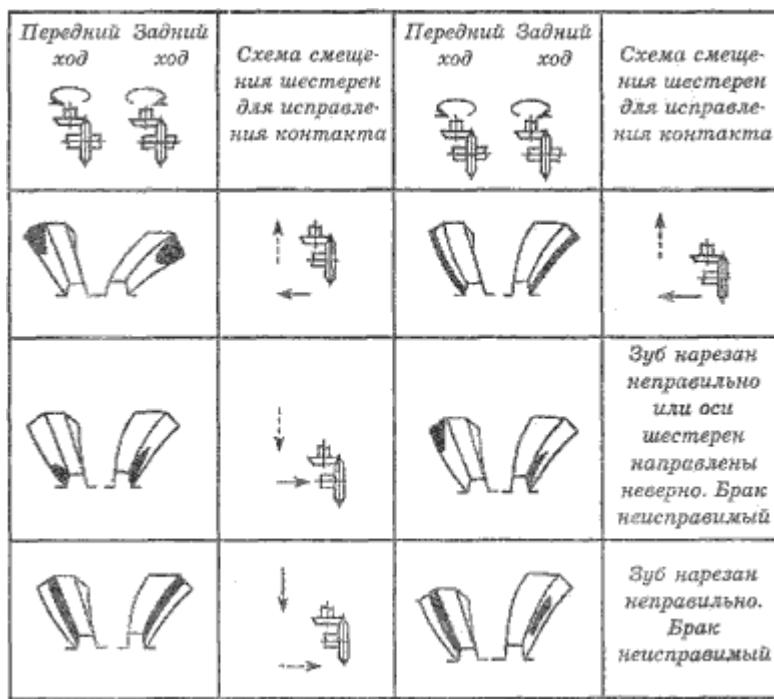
Регулировка контактов зубьев конических шестерен главной передачи
